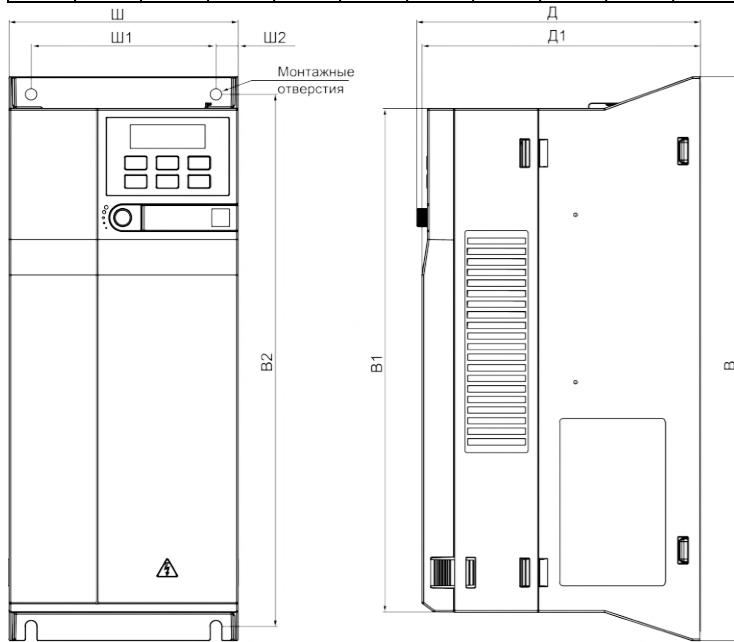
Габаритные и присоединительные размеры прибора типоразмеры 3 и 4
